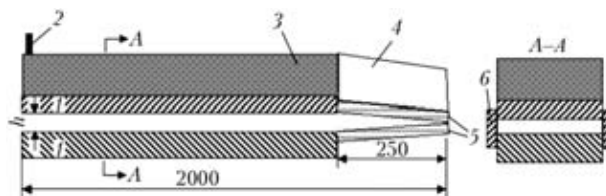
Схема сварки взрывом с ловушкой: 1 — свариваемые листы из стали и титана; 2 — детонатор; 3 — заряд ВВ; 4 — песок; 5 — ловушка; 6 — боковые пластины
